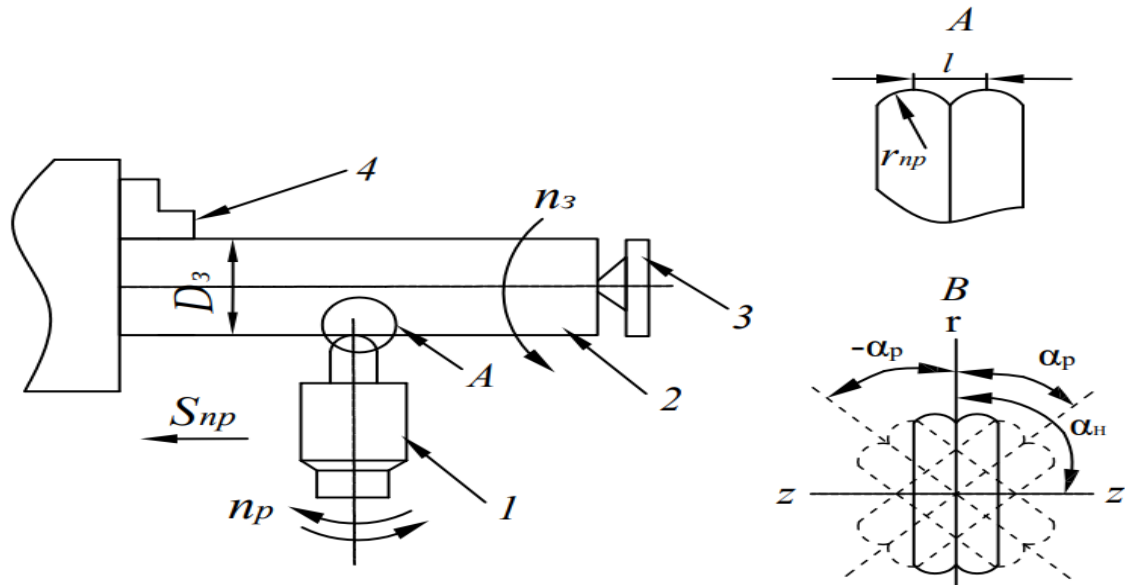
Схема реверсивного поверхностного пластического деформирования двухрадиусным роликом: 1 – рабочий инструмент; 2 – заготовка; 3 – задняя бабка; 4 – трехкулачковый патрон; А – вид вершин двухрадиусного ролика; В – схема реверсивного вращения двухрадиусного ролика
